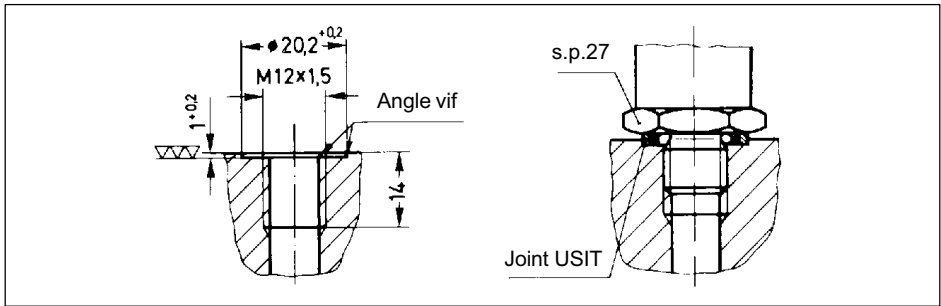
Le joint USIT U 12,7x20x1,5 fait partie des accessoires fournis avec les capteurs P3 d'une pleine échelle de 500 bars maxi. Une parfaite étanchéité nécessite une surface d'appui quasiment plane et sans stries. Le trou du tenon ne doit pas avoir de chanfrein et ne doit être que légèrement ébavuré, car la pression de l'agent de mesure presse les lèvres d'étanchéité contre le capteur et la surface d'appui.
